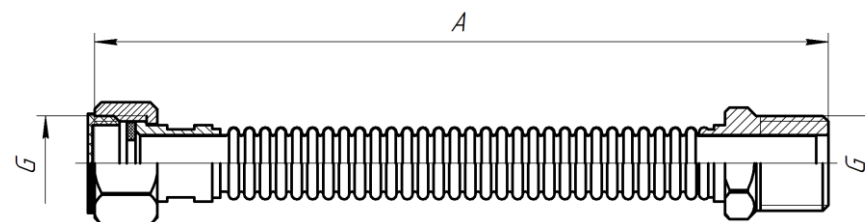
Габаритные и присоединительные размеры подводки вн-нар
